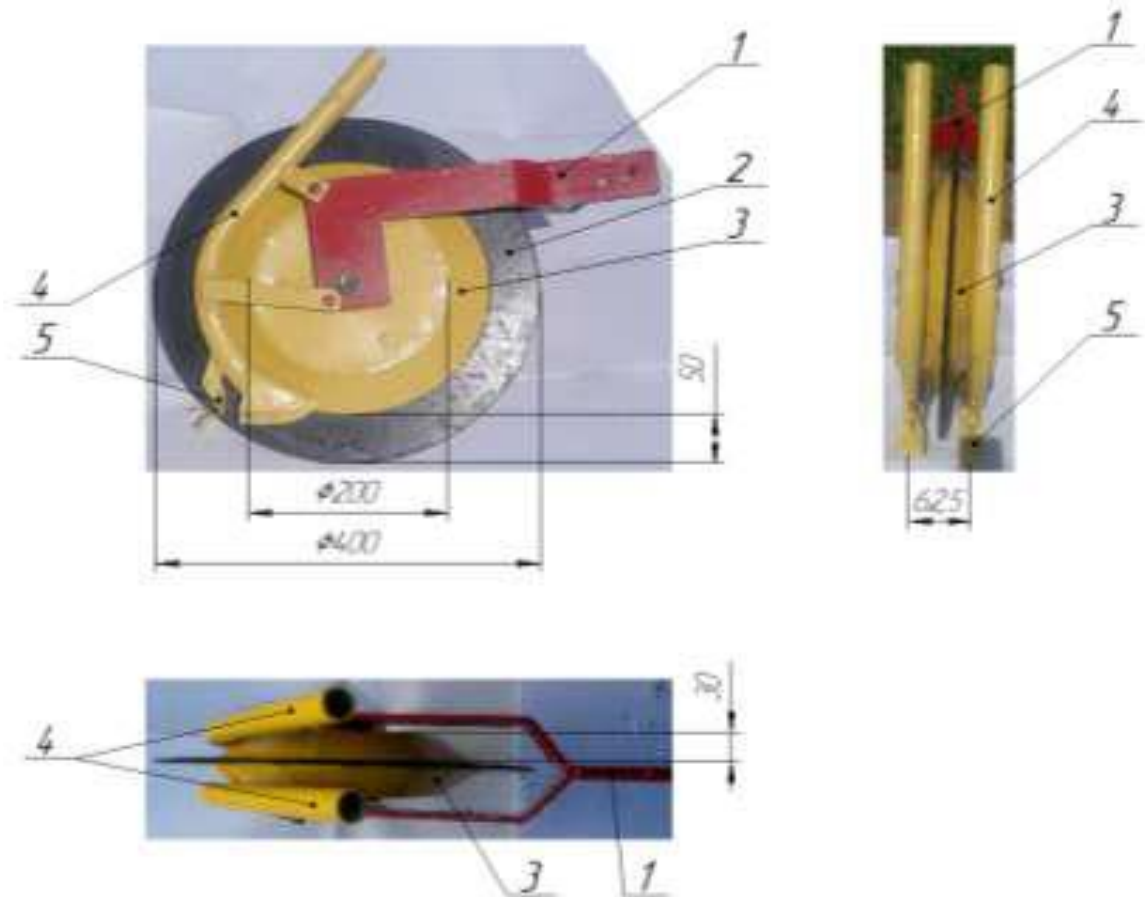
Новий макетний зразок однодискового сошника із зовнішніми симетричними ребордами-борозноутворювачами (варіант 3): 1 – корпус сошника; 2 – диск; 3 – реборда-борозноутворювач; 4 – насіннепровід; 5 – клапан насіннепровода.
